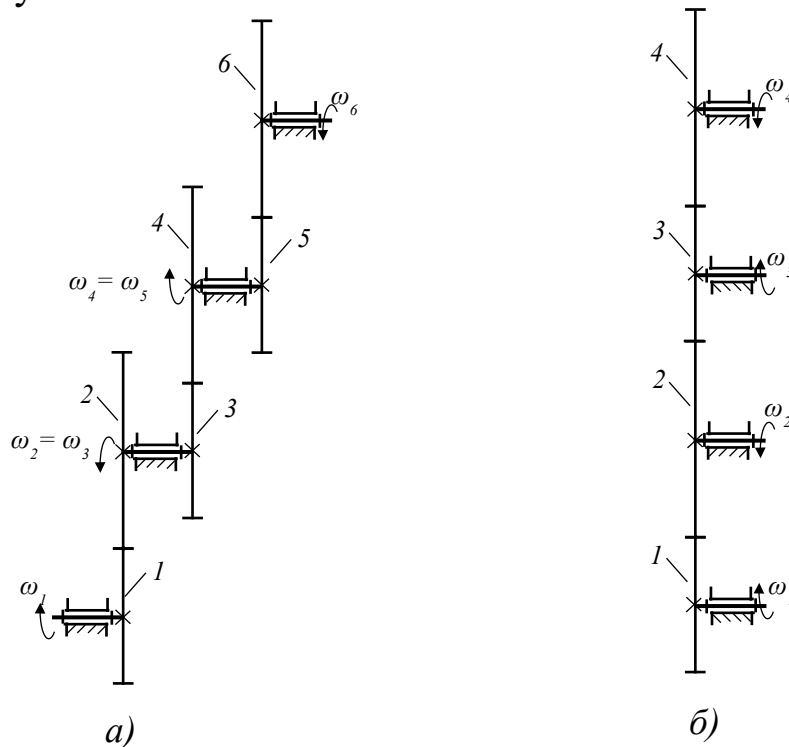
Схеми БЗМ з нерухомими осями зубчатих коліс
